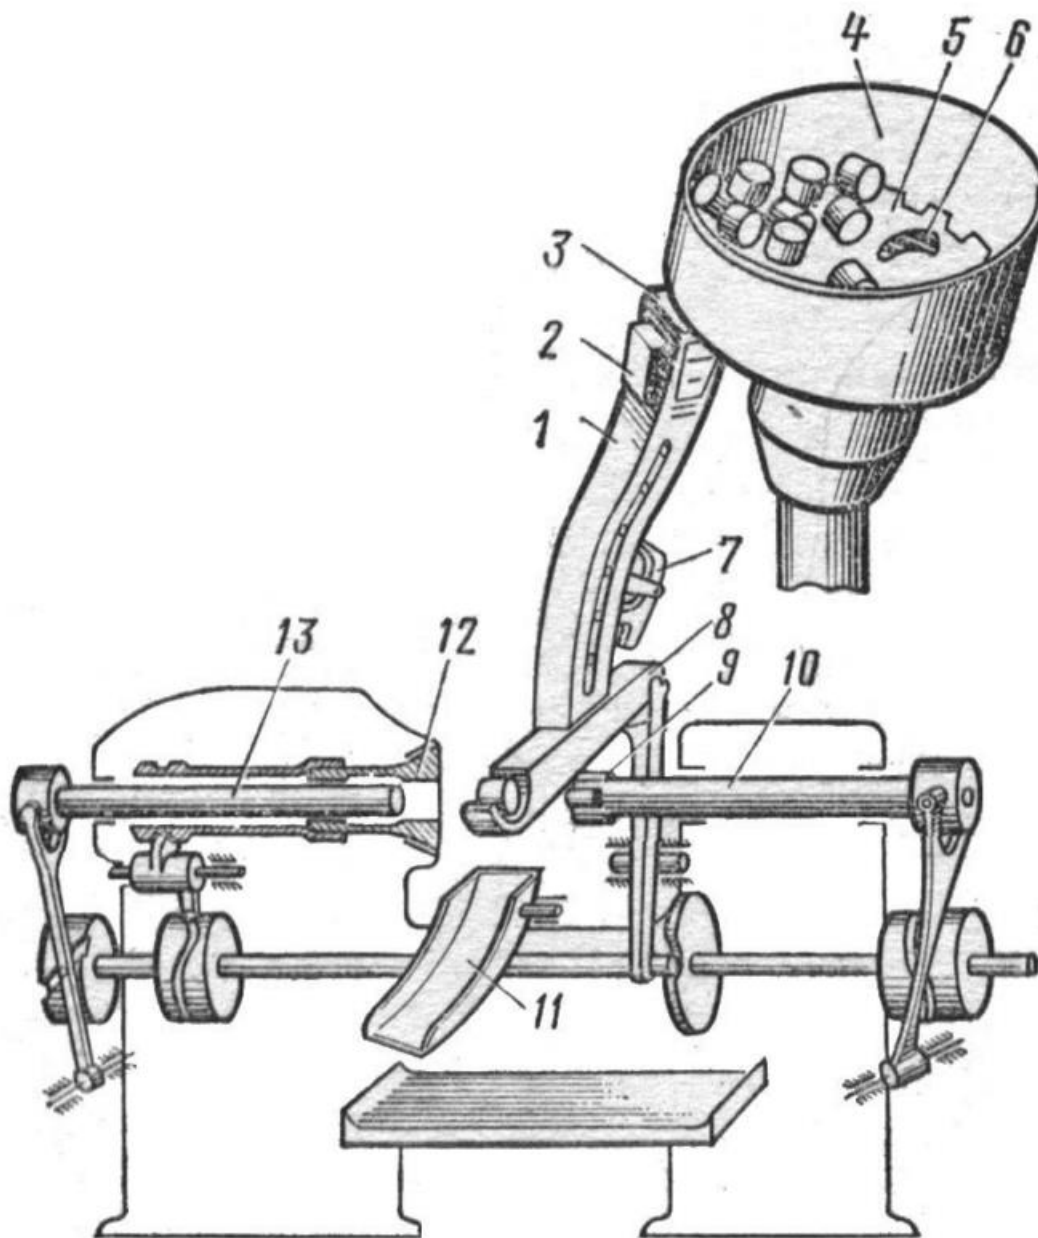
Приклад конструкції бункерного завантажувального пристрою
